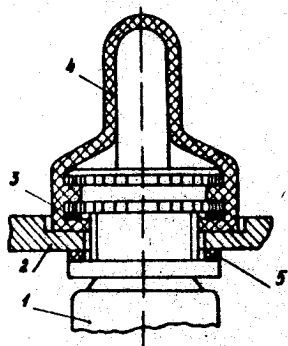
Ущільнення рукоятки тумблера за допомогою гумового ковпачка: 1- тумблер; 2- лицьова панель; 3- металева шайба; 4- ковпачок; 5- гумова прокладка
